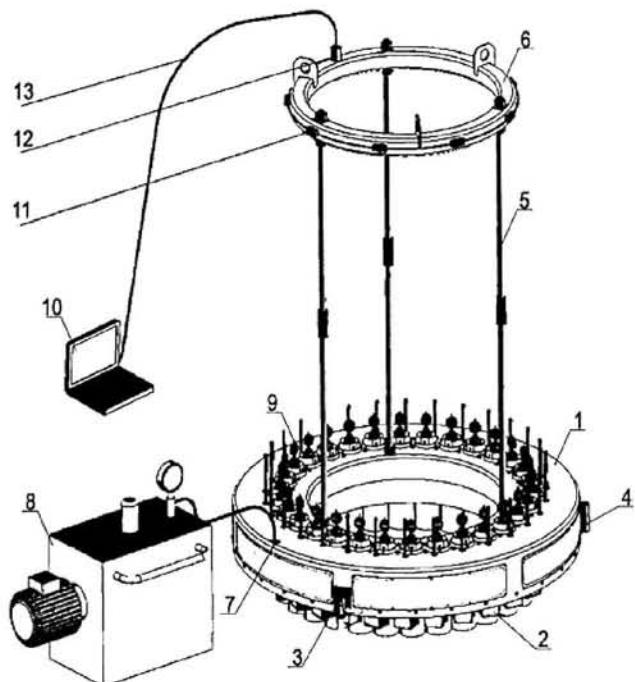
Устройство автоматической герметизации главного разъема ГЧН
